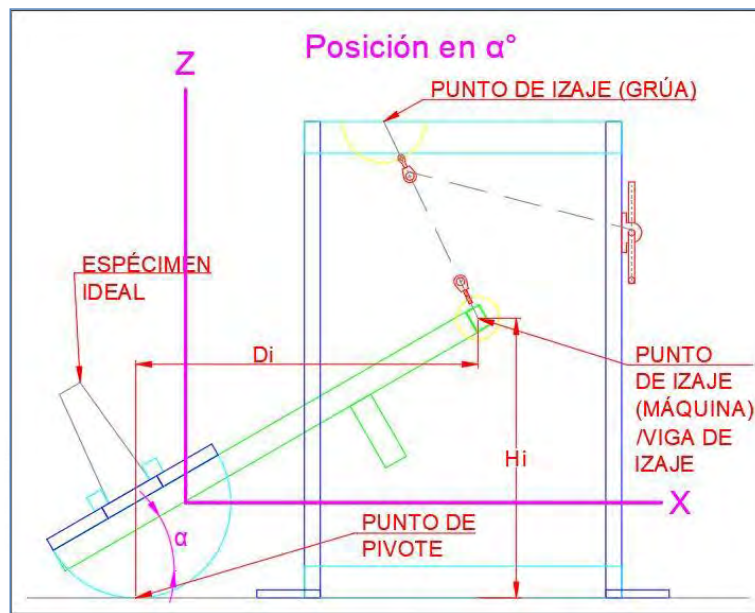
Vista frontal del mecanismo (máquina, espécimen y grúa pórtico) en movimiento
